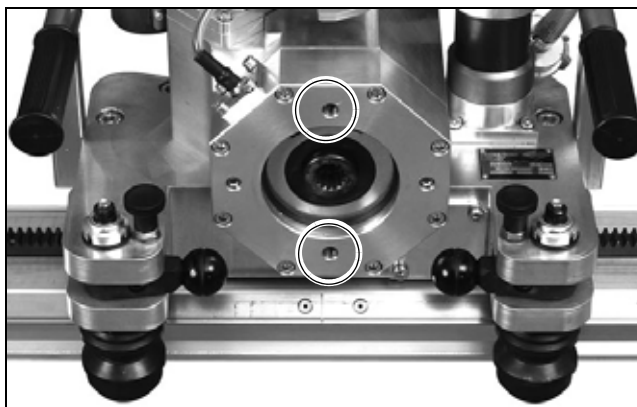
Резьба для крепления гидравлического приводного двигателя отрезного диска на корпусе пилы
